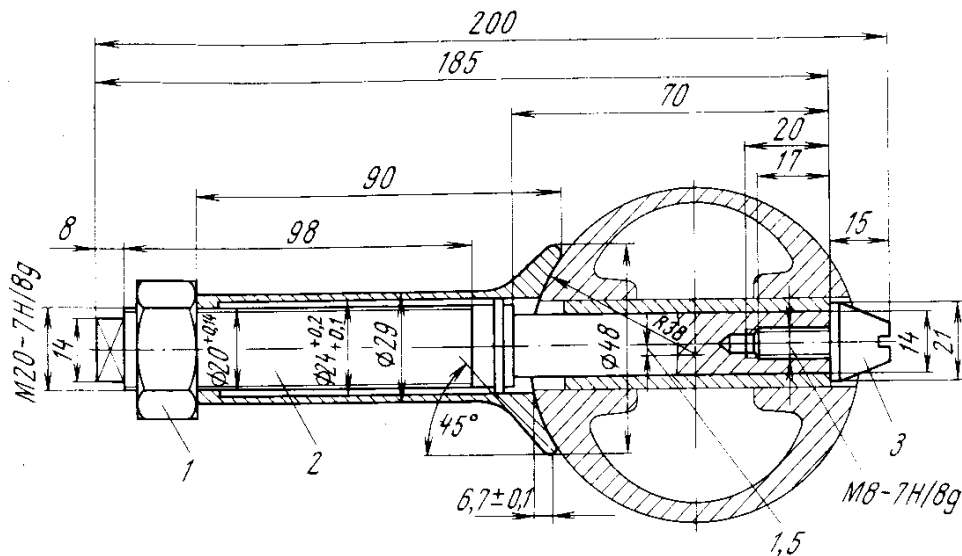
Приспособление для выпрессовки поршневого пальца: 1 — гайка; 2 — оправка; 3 — наконечник
